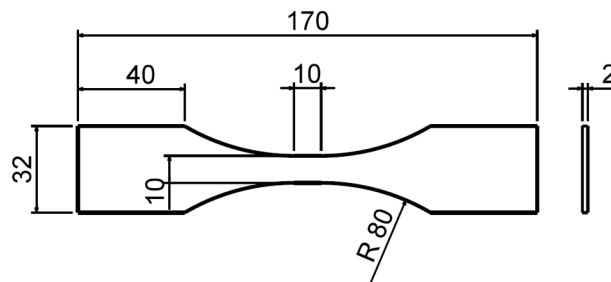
Schéma des éprouvettes, dimensions finales (en millimètres) après polissage.
